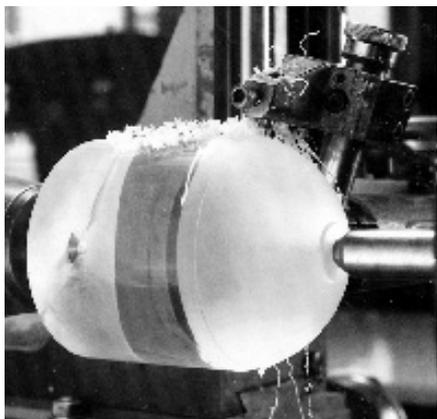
Drehen einer Kugel aus PLEXIGLAS® GS Rundstab mit Kugeldrehvorrichtung
